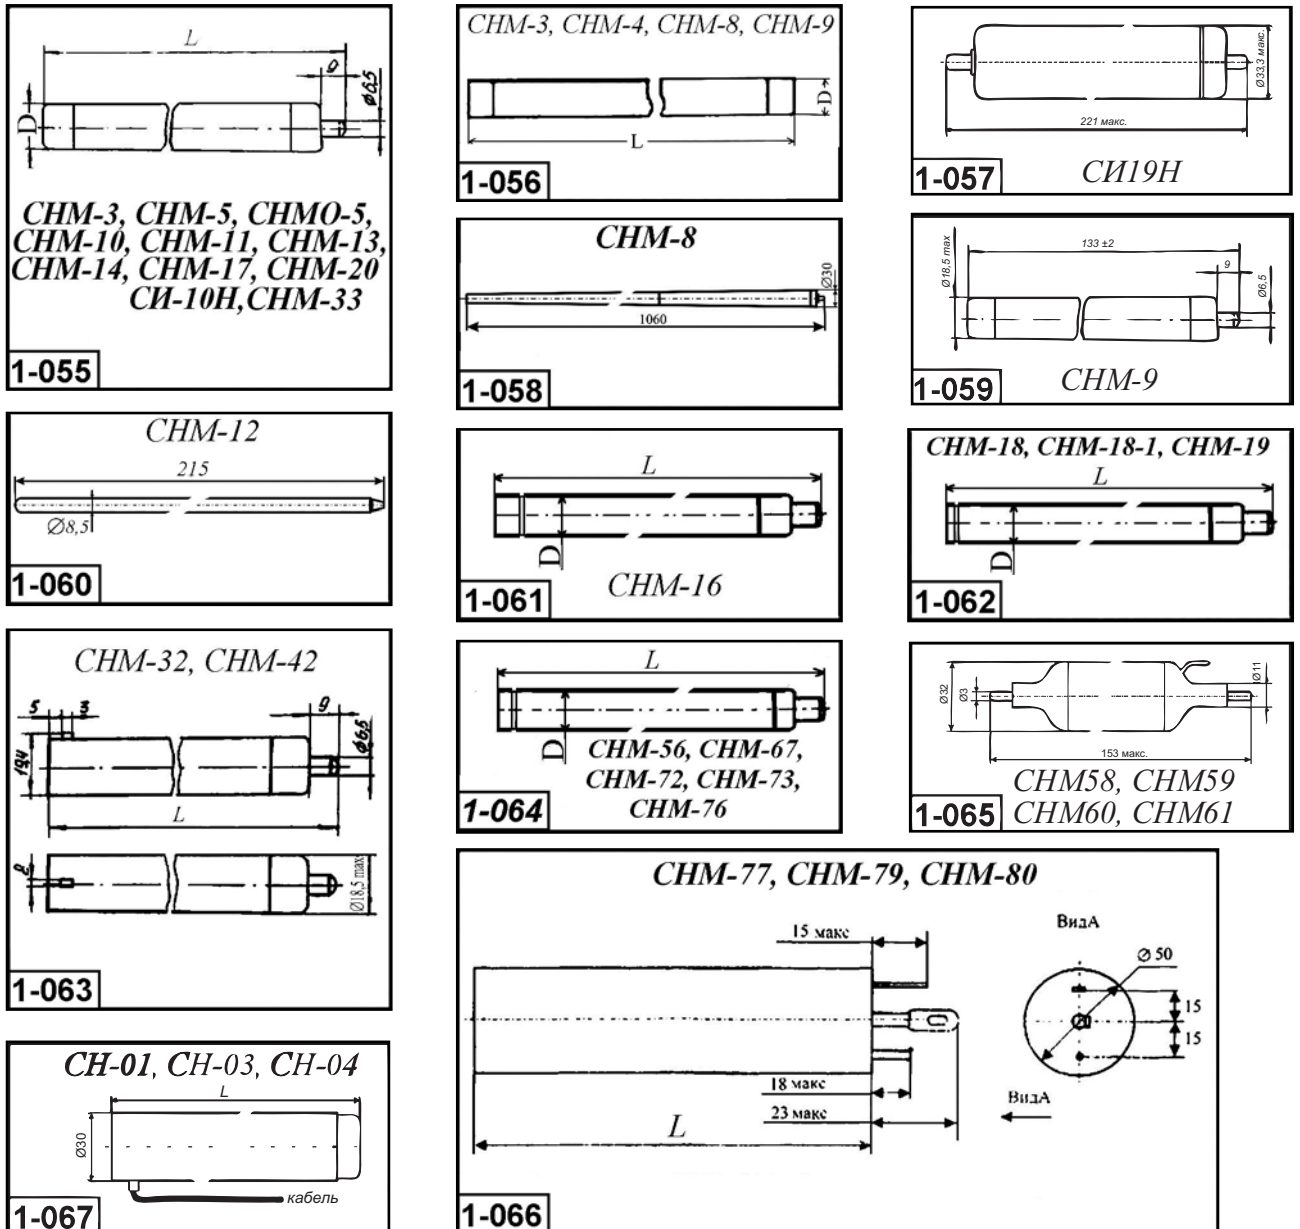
Внешний вид и габаритные размеры детекторов нейтронов
